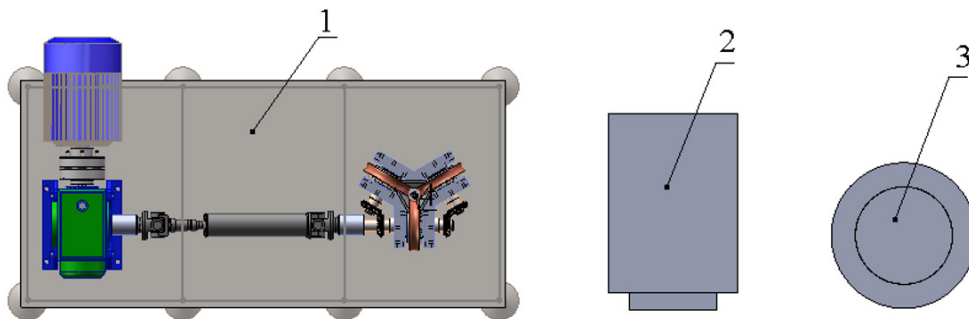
Схема розташування установки валкової розливки-прокатки і допоміжного обладнання
